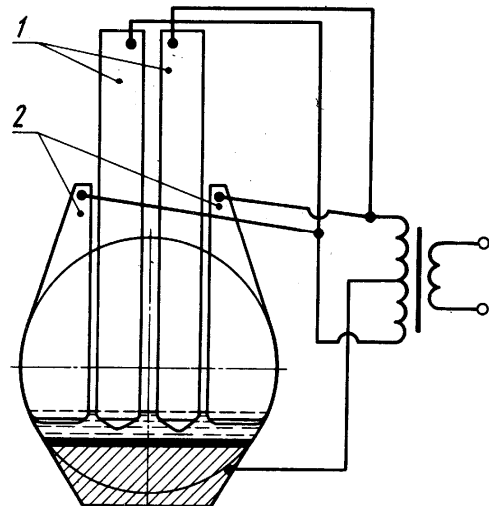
Электрошлаковая сварка вала по бифилярной схеме
